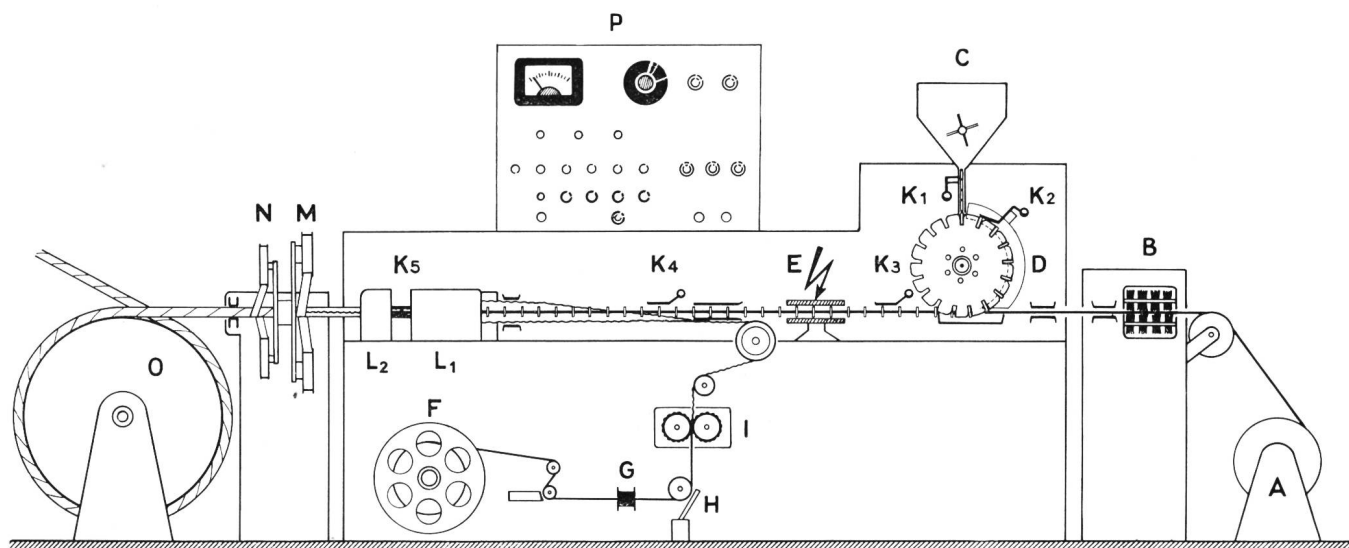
Schéma de la machine à fabriquer la paire coaxiale
